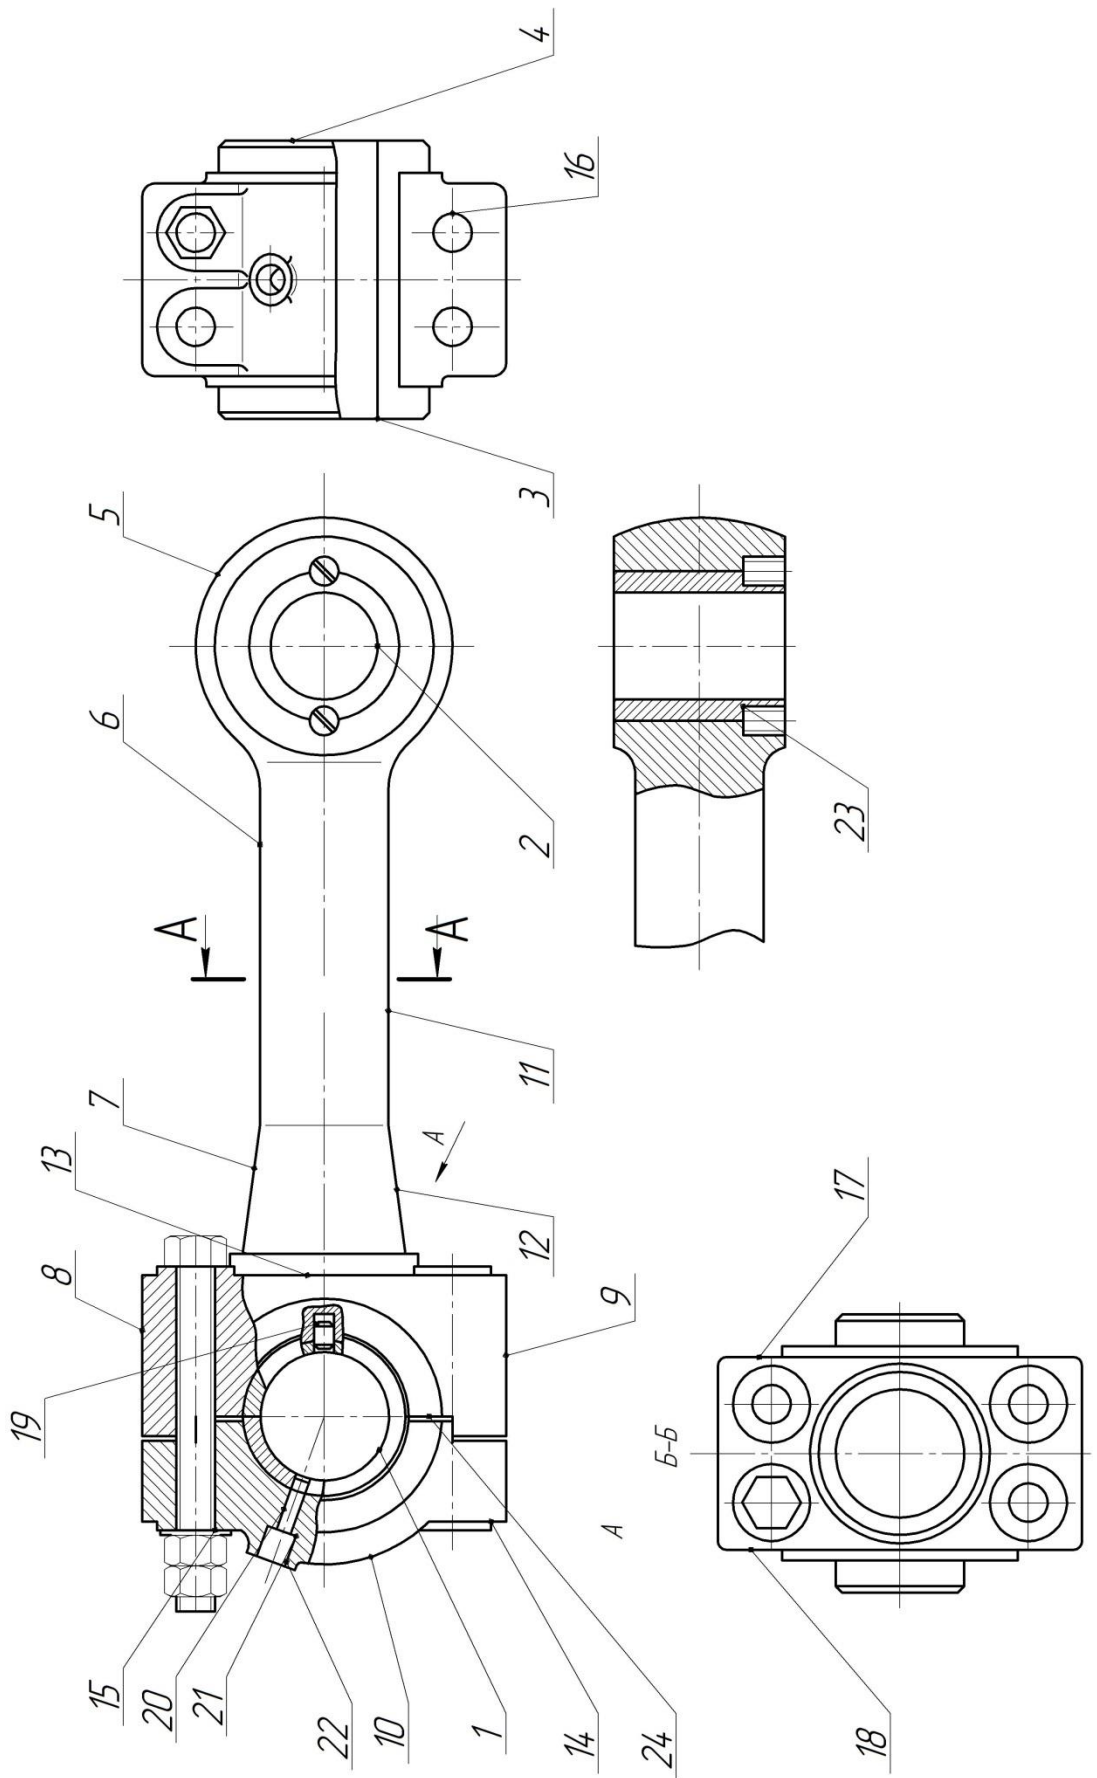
Деталь - «Тяга сборная», кодированный чертеж
